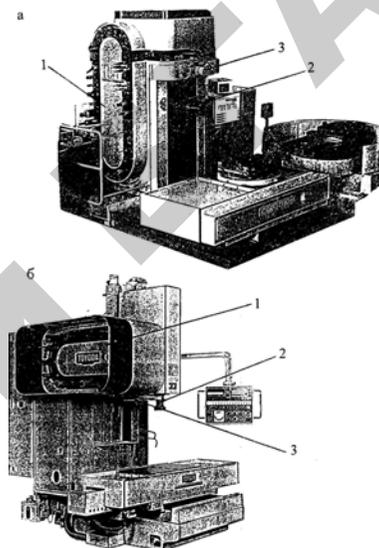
Конструктивное исполнение обрабатывающих центров со встроенными цепными магазинами:
